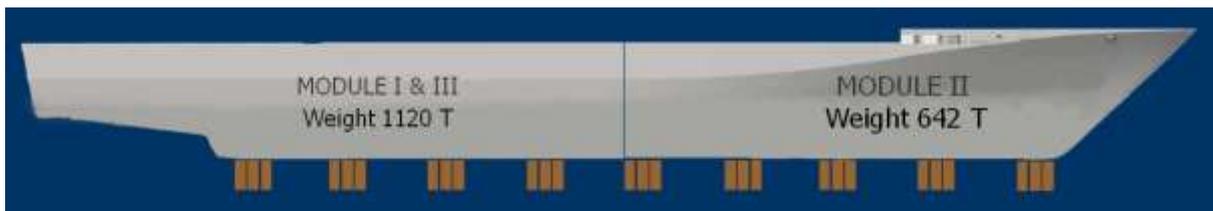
Rencana tahapan proses *Sub Assembly*, *Assembly*, dan *Grand Assembly* pada *Assembly Hall*.
